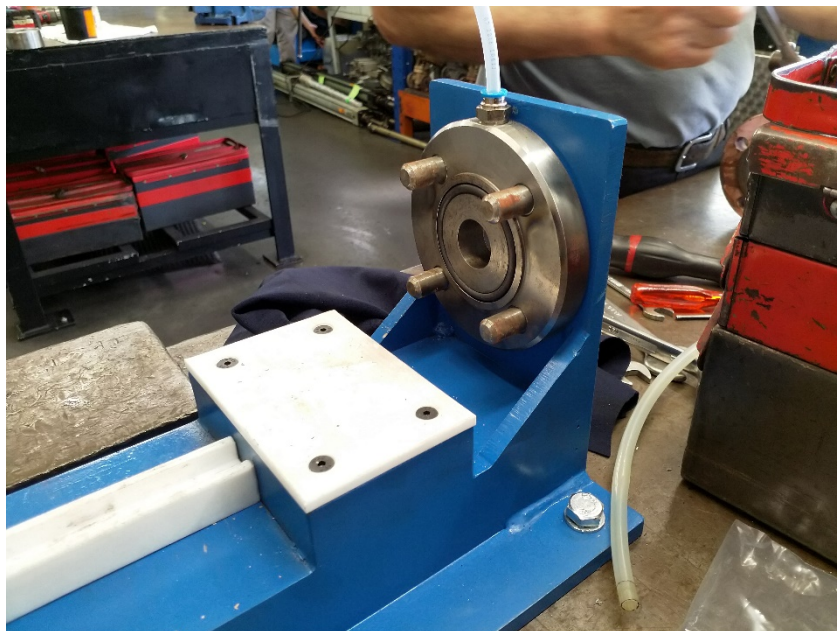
Equipamento de teste já fabricado – vista nº4.
